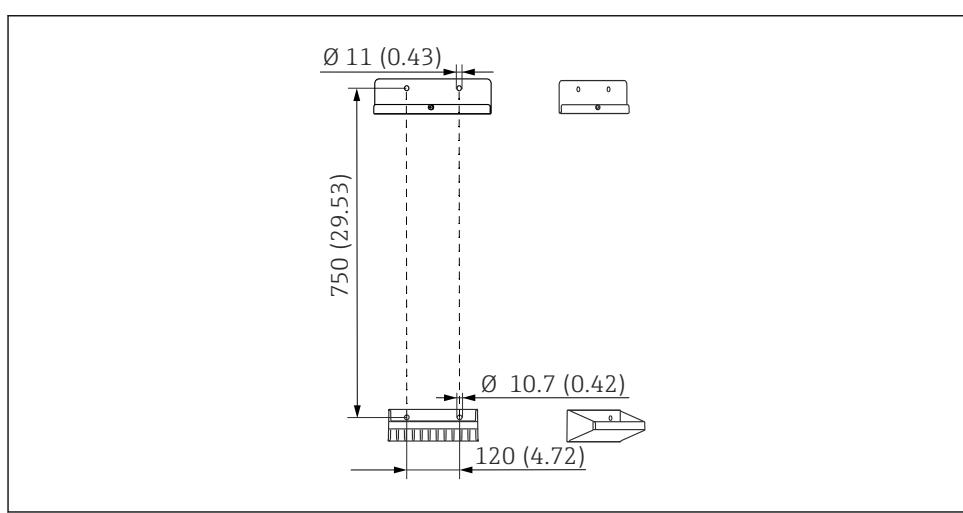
安装架的外形尺寸示意图; 单位: mm (in)
